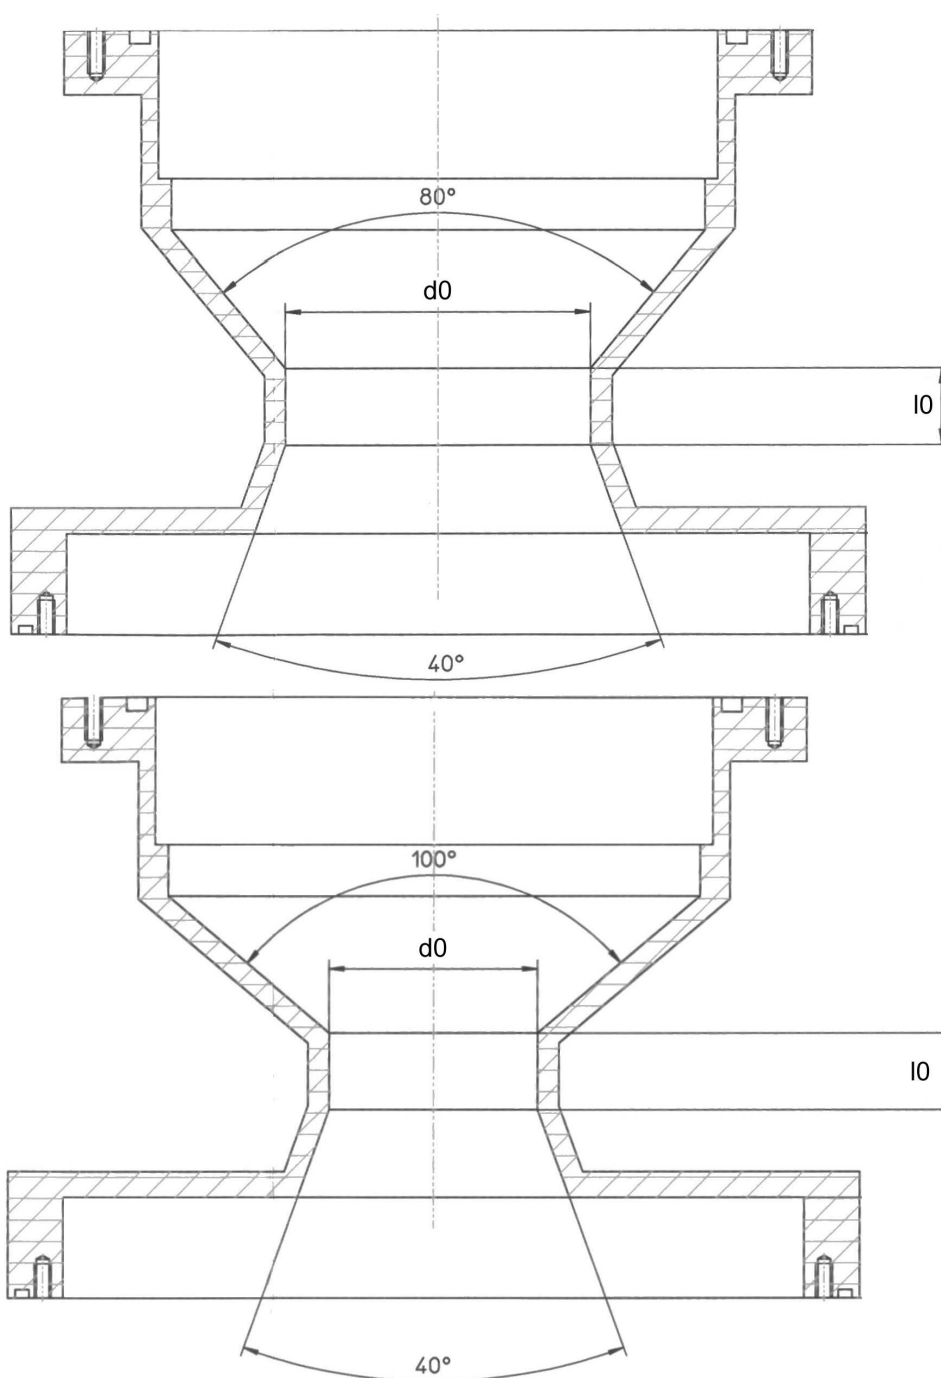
Plans des embouts secondaires (en haut : embout n°1 - en bas : embout n°2)
